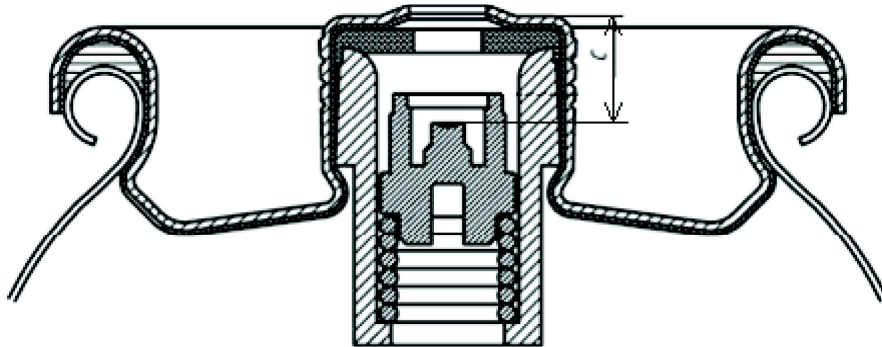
Schnitt durch ein Ventil mit Gewindedom (Typ 1)
